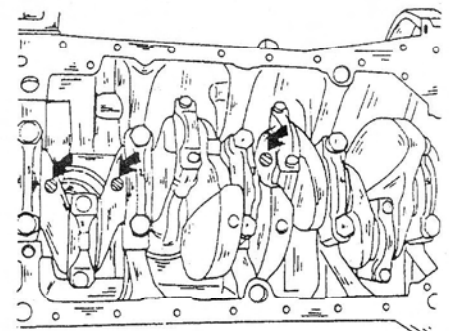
Стрелки указывают на цветные точки на коленах коленчатого вала. Они определяют размер вкладышей подшипников в крышках.
